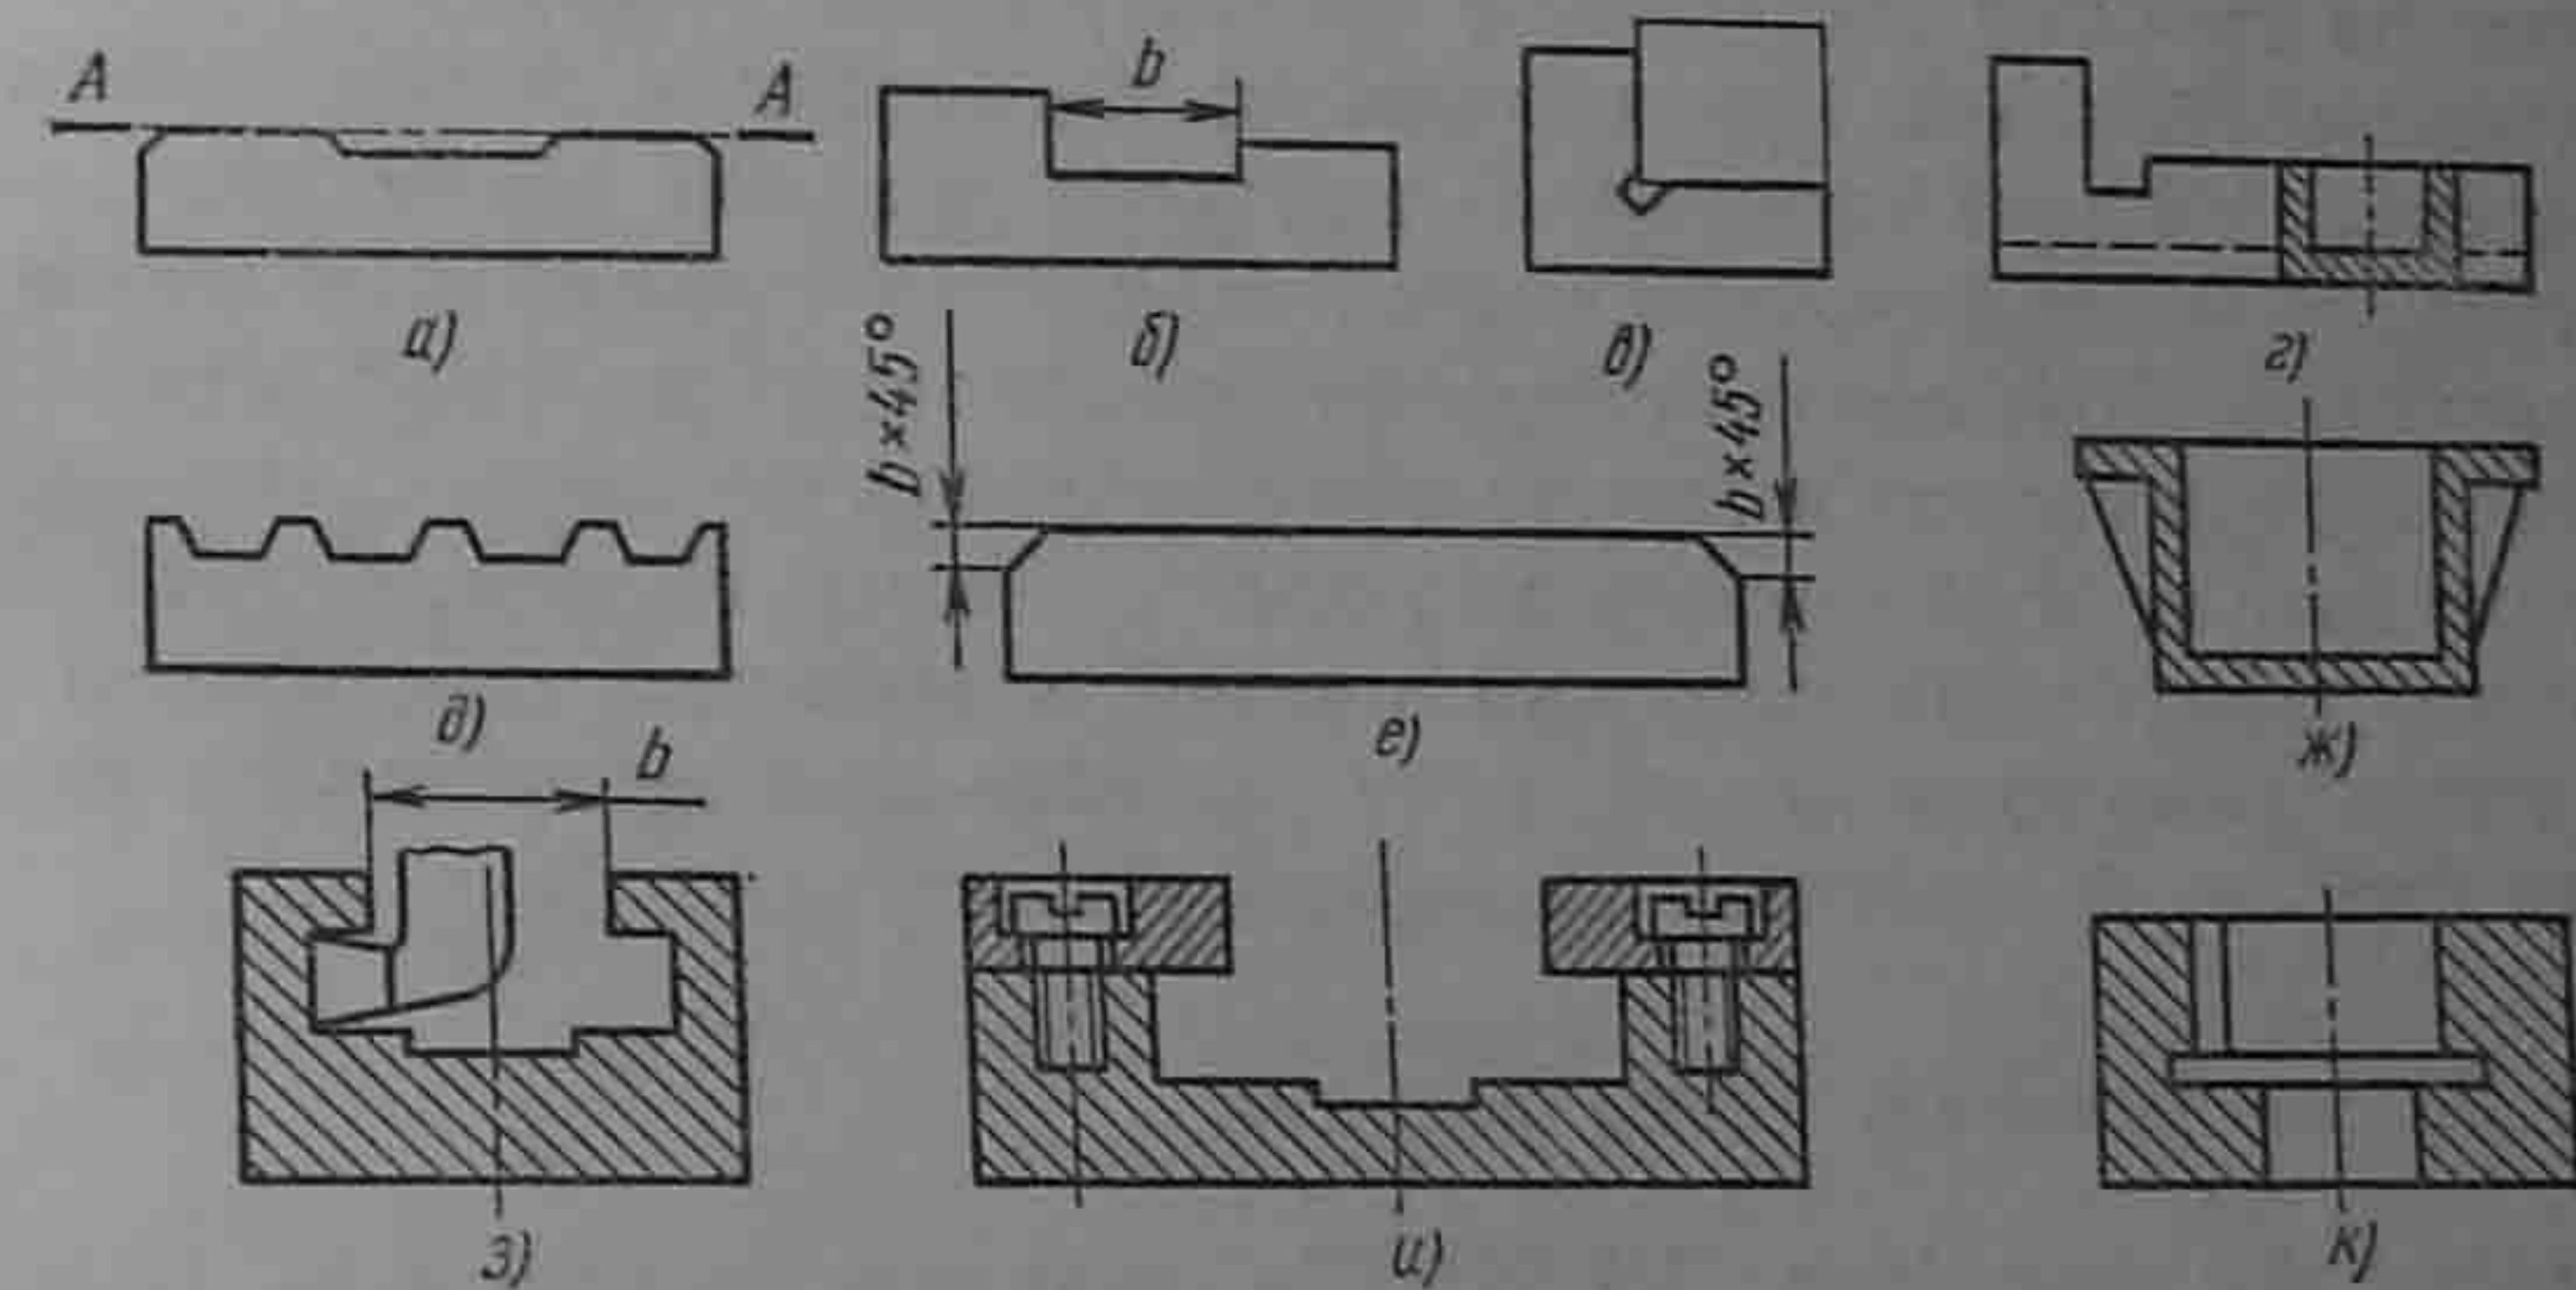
Примеры конструкций деталей машин, обрабатываемых на строгальных станках
